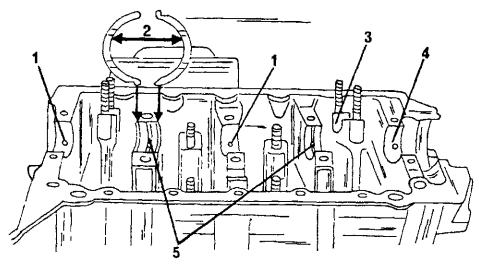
Установка коленчатого вала на двигателе типа TU.
